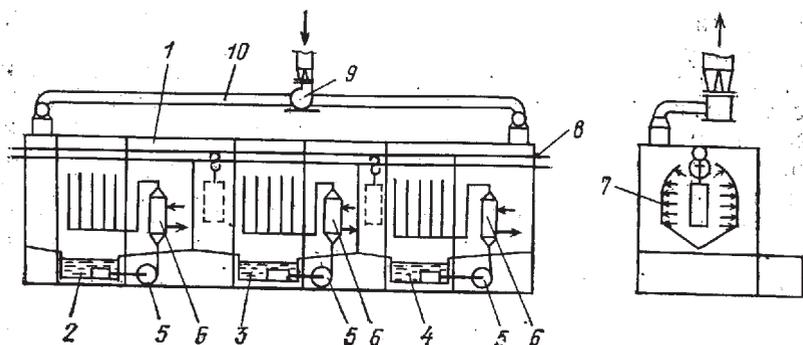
Схема агрегата струйной подготовки поверхности:
